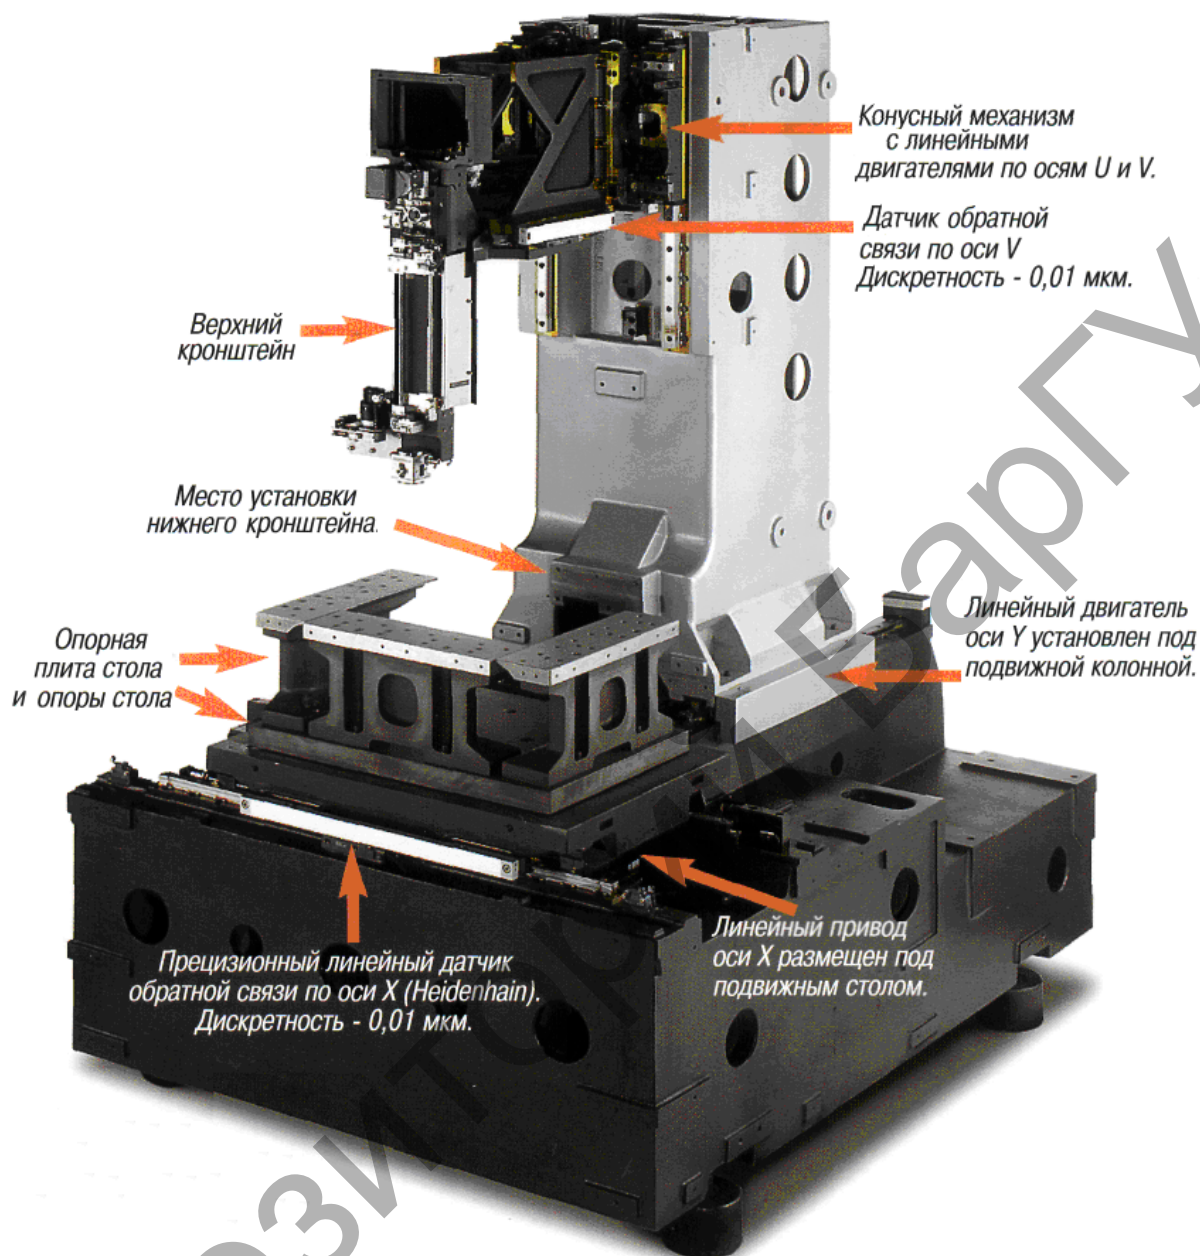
Основные узлы проволочно-вырезного станка фирмы “Sodick”
